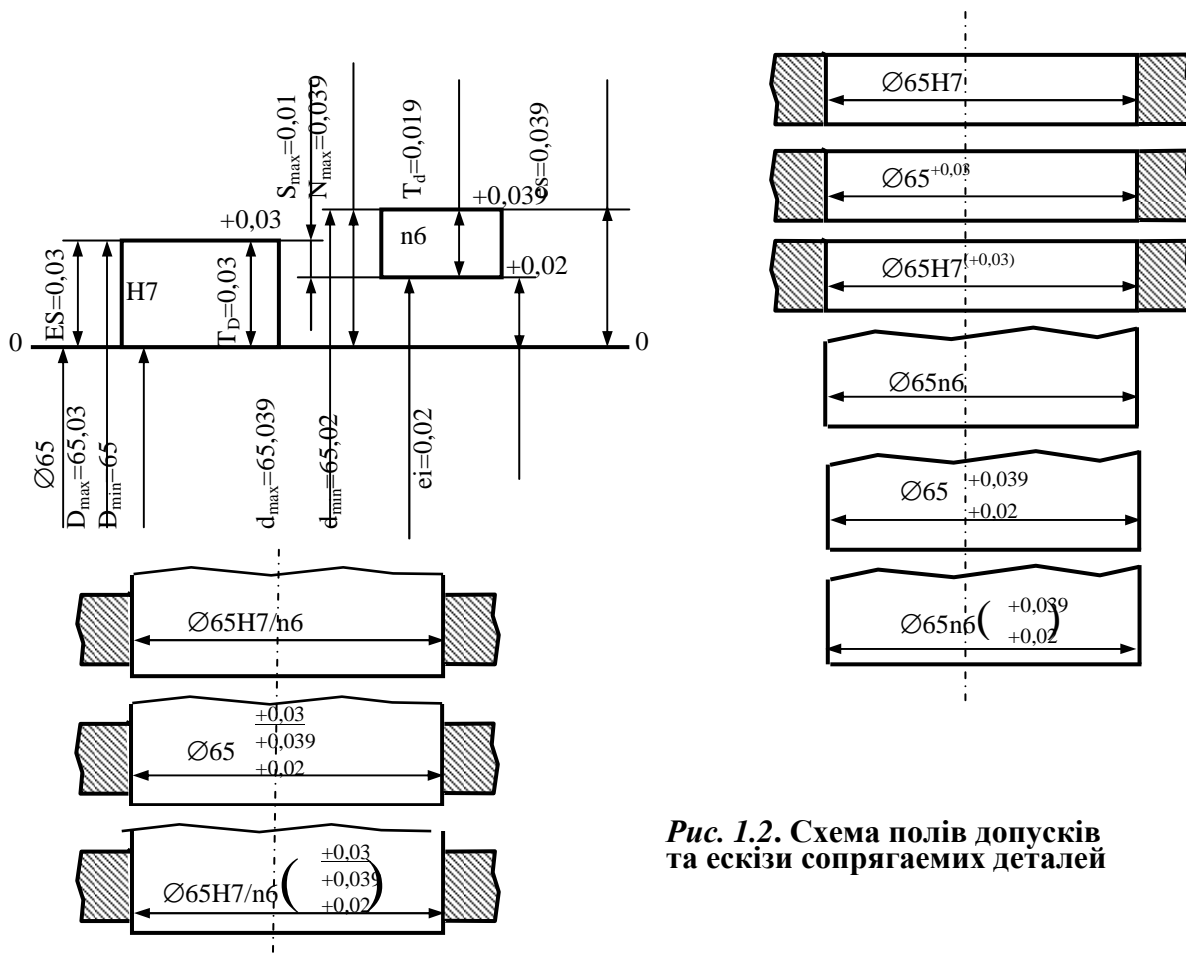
Схема полів допусків та ескізи сопрягаемых деталей
